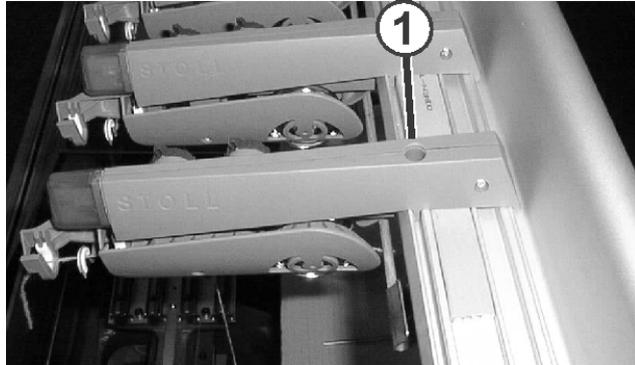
Ausbau einer Fadenkontrolleinrichtung
